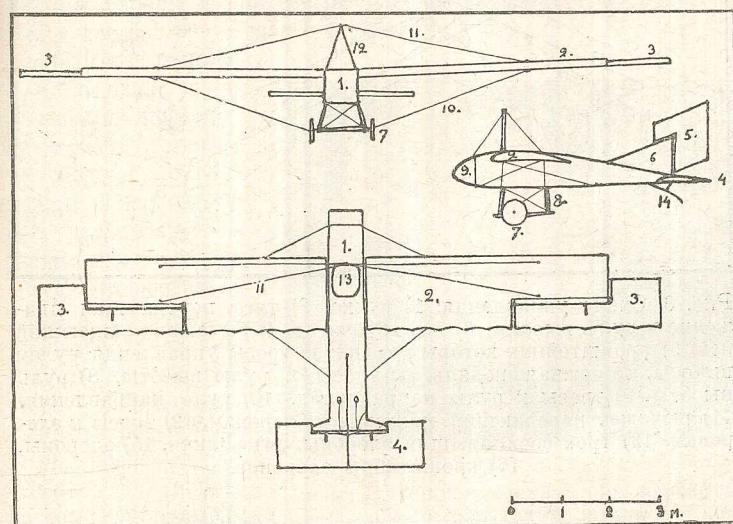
1) корпус (фюзеляж), 2) крыло, 3) руль поперечной устойчивости (элерон), 4) руль высоты, 5) руль направления 6) киль (вертикальный стабилизатор), 7) колесо, 8) стойка шасси, 9) съемная коробка из фанеры, закрывающая переднюю часть корпуса, 10) несущая растяжка из стальной проволоки 2,5 м.м., 11) поддерживающая растяжка 2 м.м., 12) кабин из 2-х стальных труб, 13) помещение пилота.
